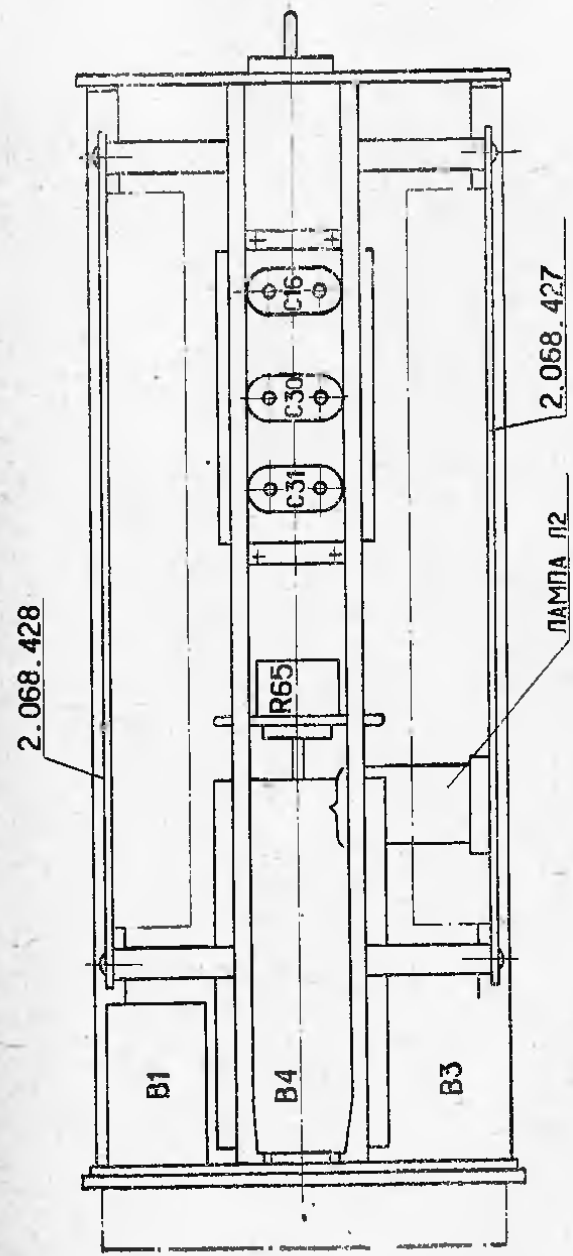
Схема расположения установочных элементов блока развертки (вид сверху)
